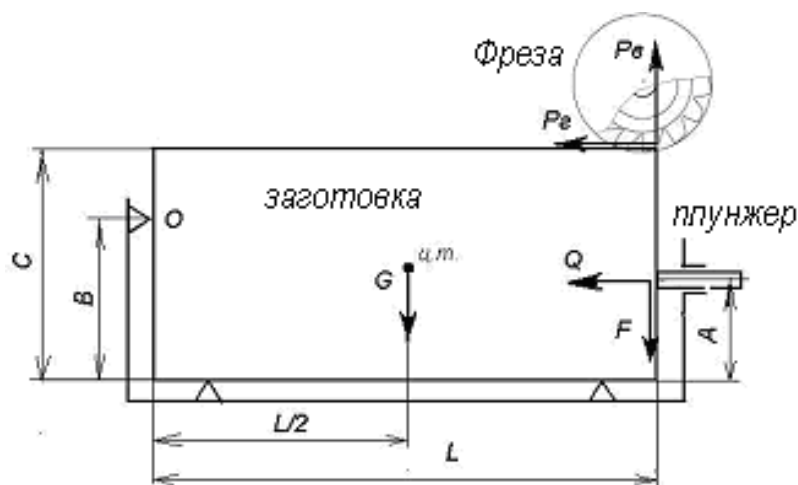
Розрахункова схема при фрезеруванні площини
